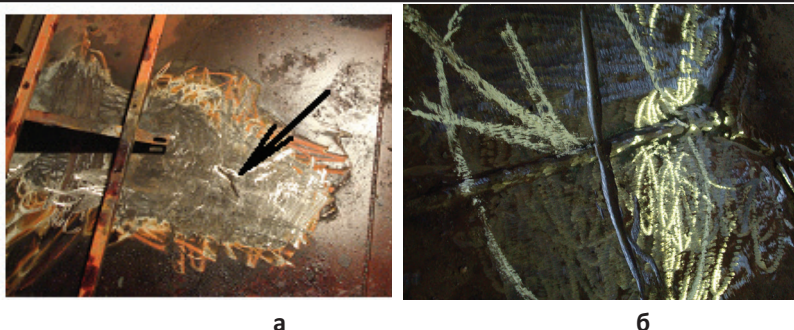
Характерные трещины в листовом металле а и сварочном шве б автоцистерны
